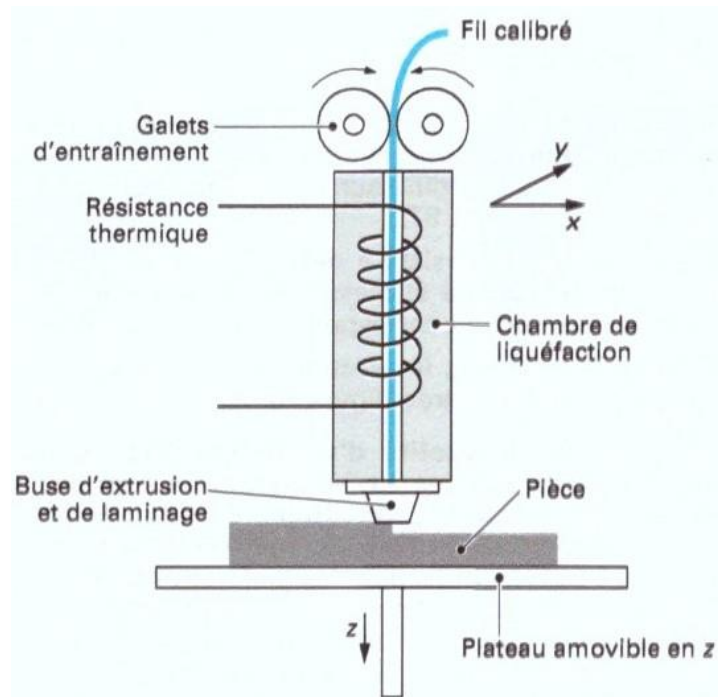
Principe du procédé Extrusion et laminage d'un filament.
